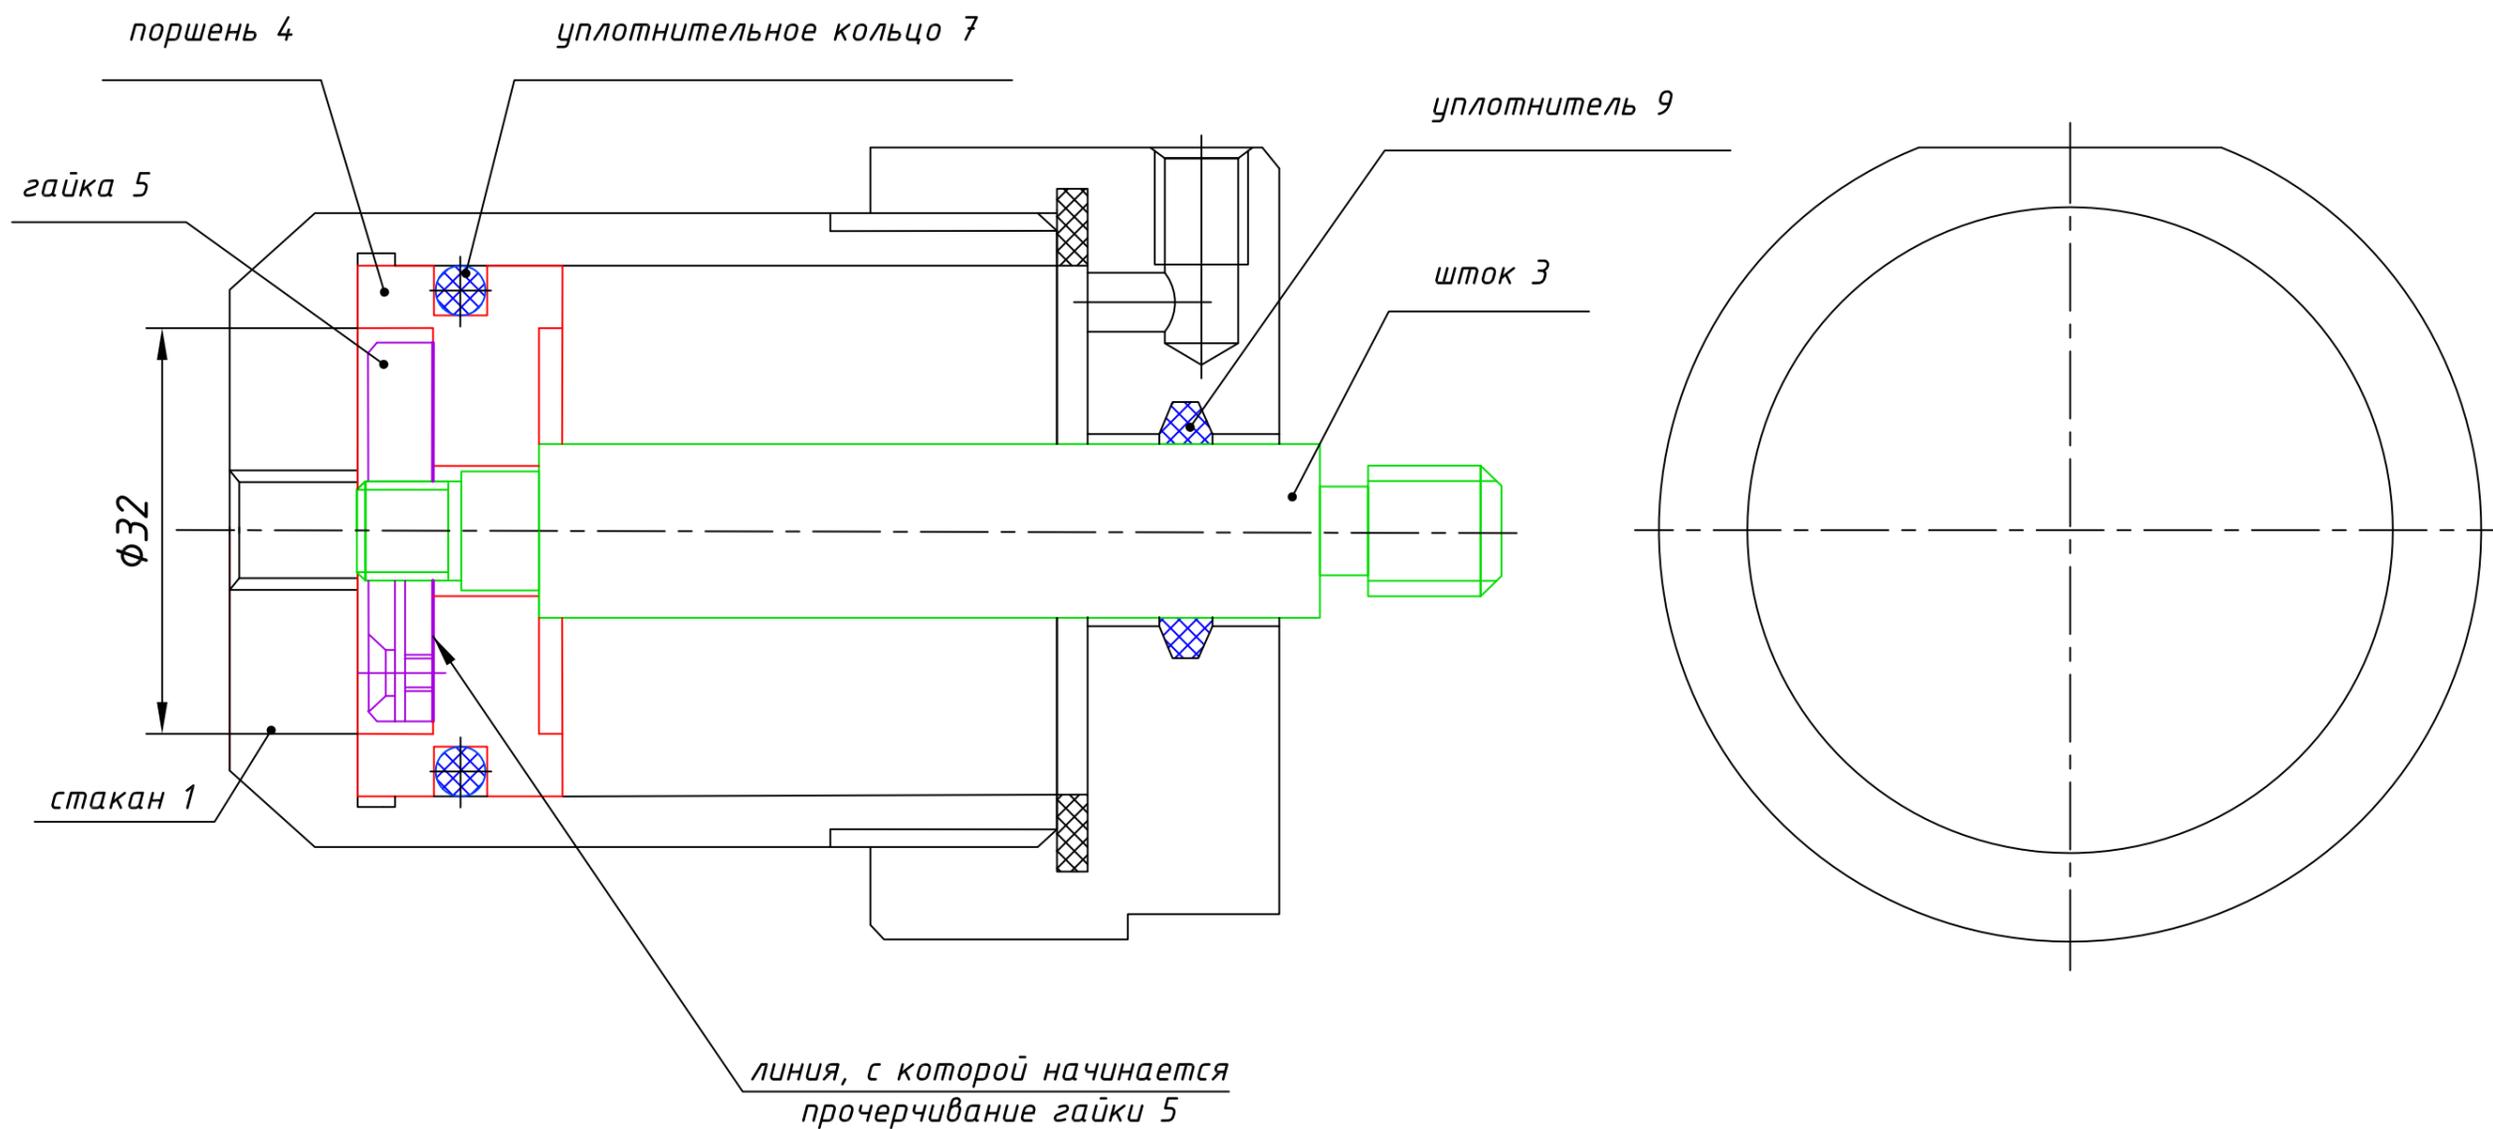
Установка на резьбовой конец штока 3 гайки 5.
